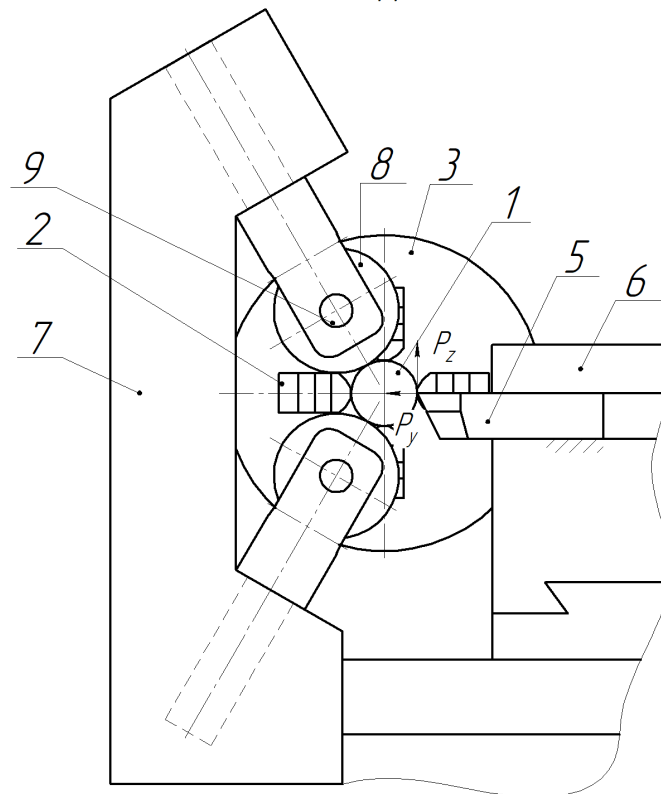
Схема токарного оброблення деталей з додатковими опорами, що представлені у вигляді двох роликів та конуса задньої бабаки
